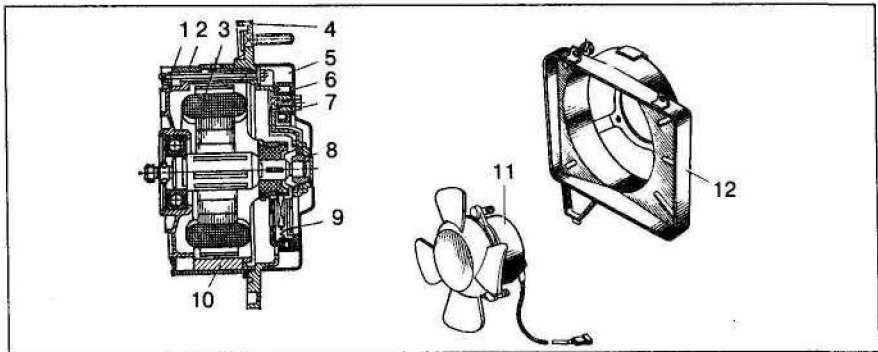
Электродвигатель МЭ272 вентилятора системы охлаждения двигателя: 1 — стяжной болт; 2 — корпус; 3 — якорь; 4 — крышка; 5 — кожух; 6 — щеткодержатель; 7 — болт крепления щеткодержателя; 8 — втулка подшипника якоря; 9 — щетка; 10 — постоянный магнит (полюс); 11 — вентилятор с двигателем в сборе; 12 — кожух вентилятора
